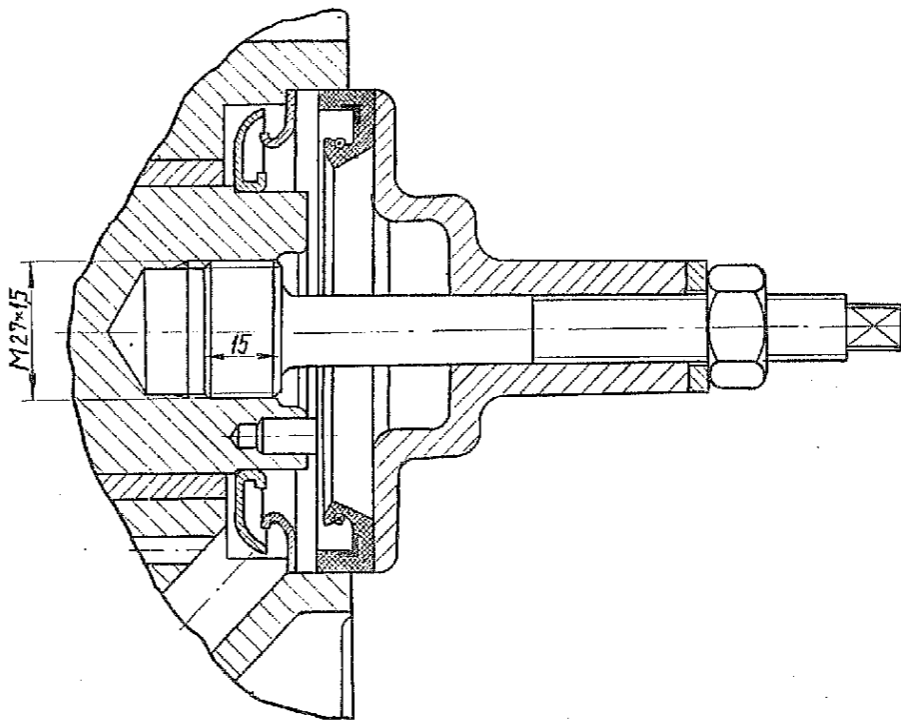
Оправка для запрессовки сальника коленчатого вала со стороны маховика
